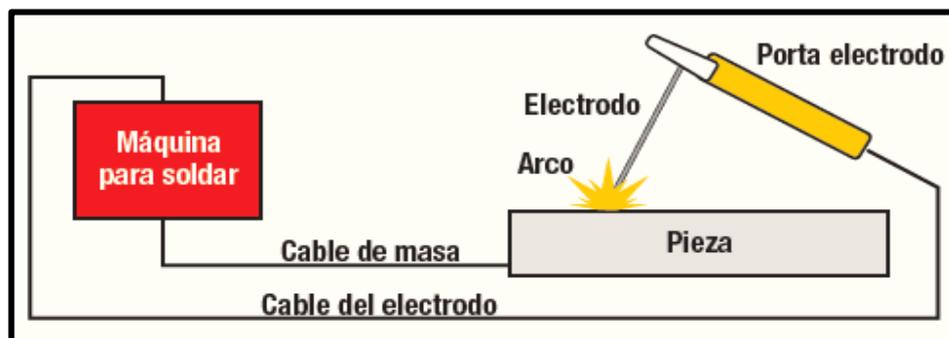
Esquema general de soldadura por arco eléctrico
